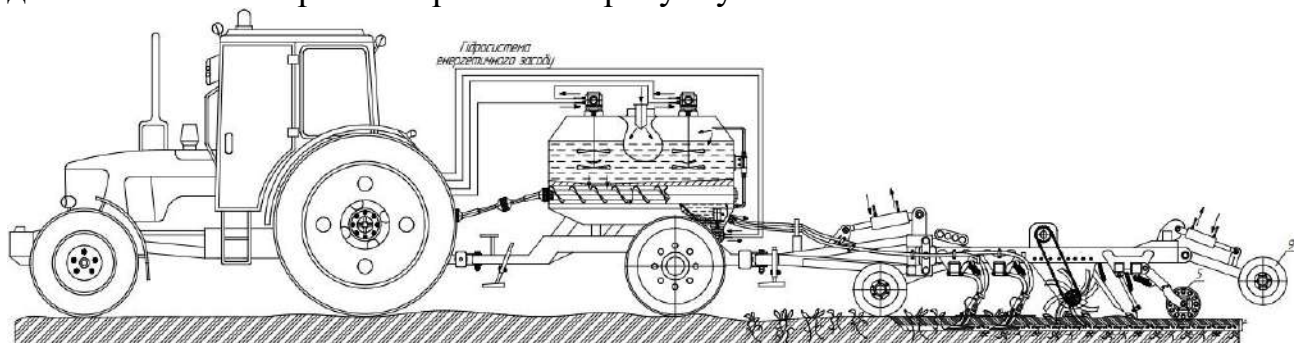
Загальний вигляд машинно-тракторного агрегату для технології Strip-till
